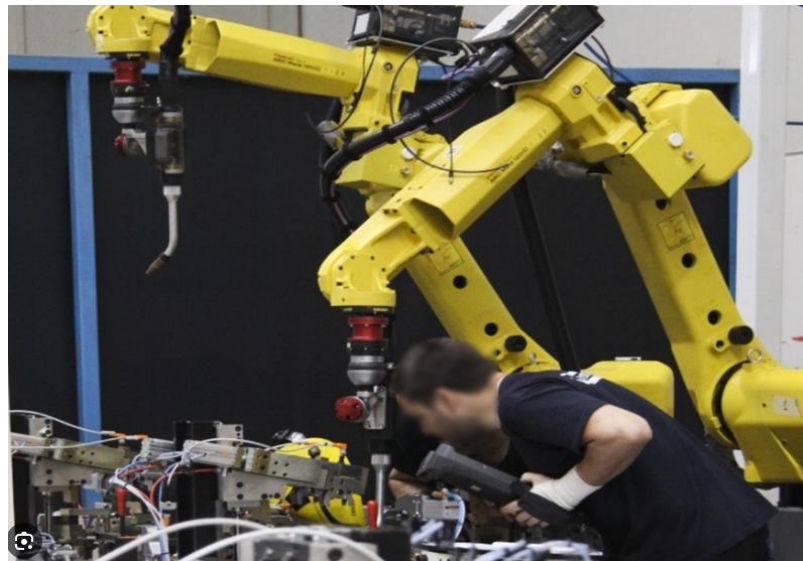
Proceso de soldadura en líneas de ensamblaje automatizada mediante robots
